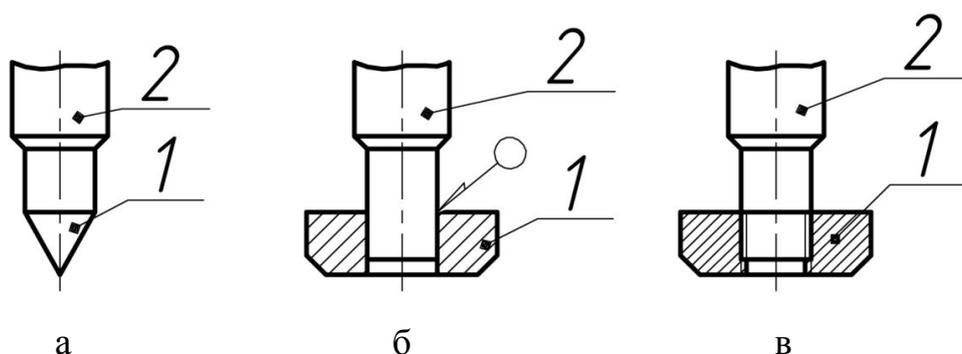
Неподвижное соединение шпинделя с клапаном:
